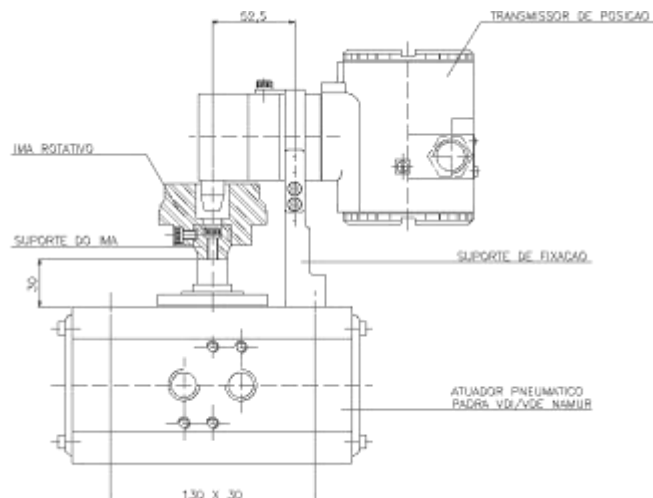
b – Desenho Dimensional do Sensor Remoto
